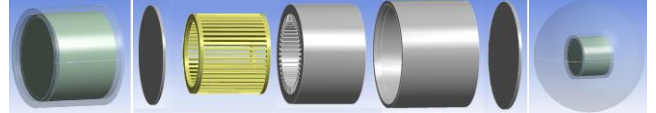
Vue éclatée de l'ensemble des éléments de la structure
